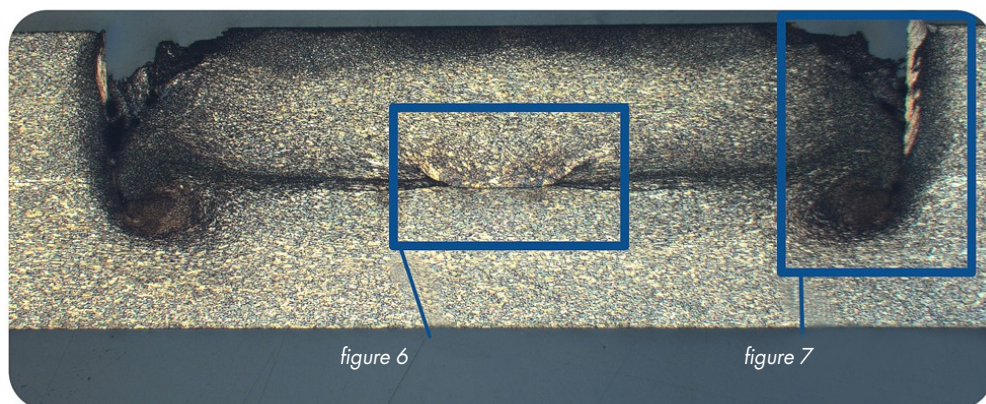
coupe métallographique d'un assemblage typique de la série 1 (conditions de soudage: temps de soudage: 4 sec.; profondeur de pénétration: 1,9 mm; vitesse de rotation: 1.500 tr/min)
